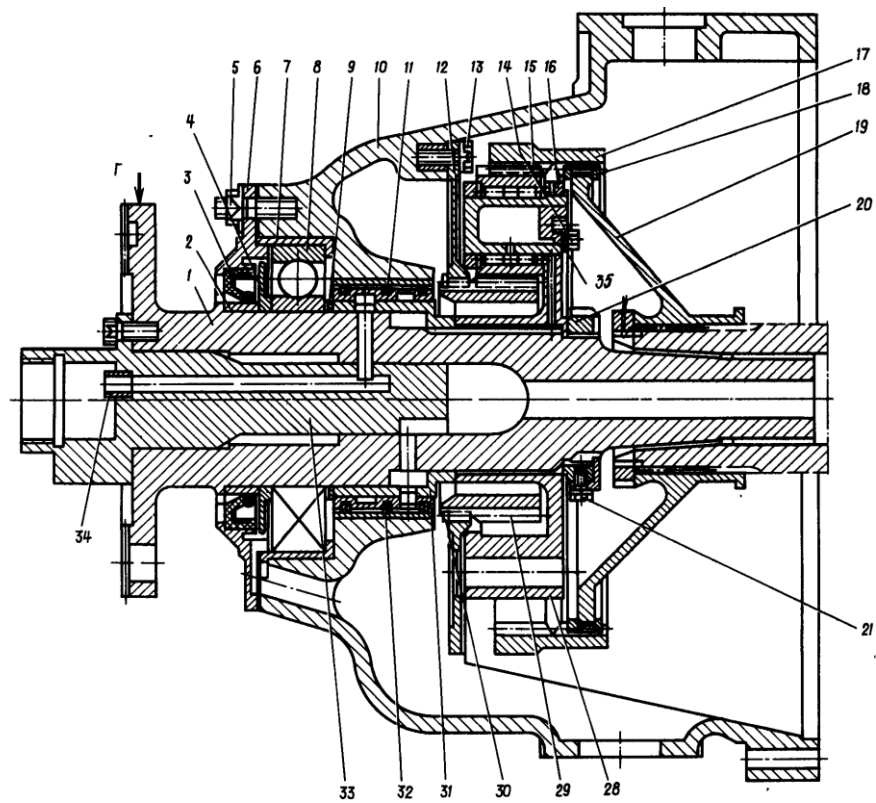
Редуктор двигуна М-14П (поздовжній розріз):
